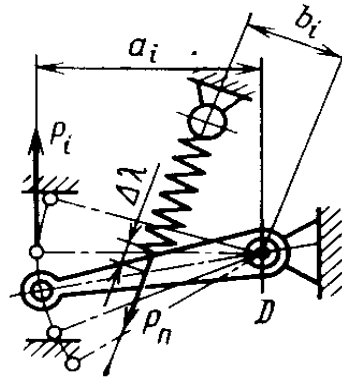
Розрахункова схема підвіски з циліндричною пружиною
